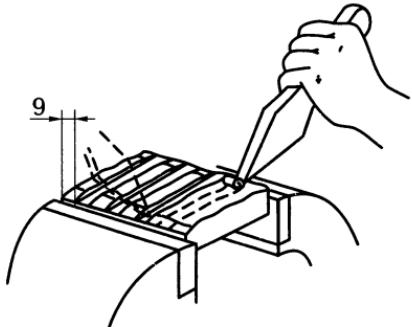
Срубание слоя металла на широкой плоской поверхности
